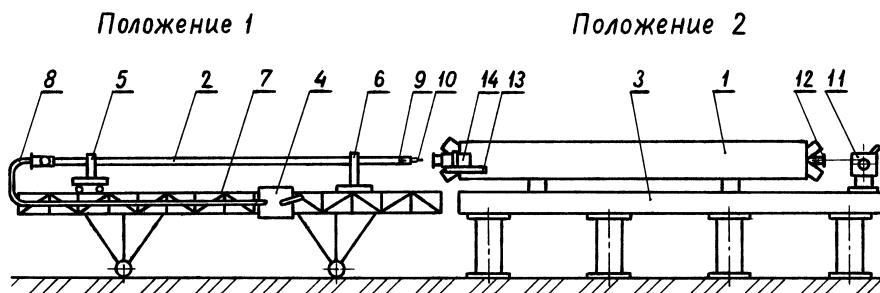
Схема ступени стенда установки камер в магниты: 1 — дипольный магнит; 2 — вакуумная камера; 3 — контрольно-сборочный стол; 4 — гидронасос; 5 — каретка; 6 — опора; 7 — передвижная тележка; 8 — дюритовые шланги; 9 — проушина; 10 — приспособление для осадки; 11 — лебедка; 12 — второй фланец камеры; 13 — кронштейн для крепления насоса; 14 — насос ПВИГ–100.
